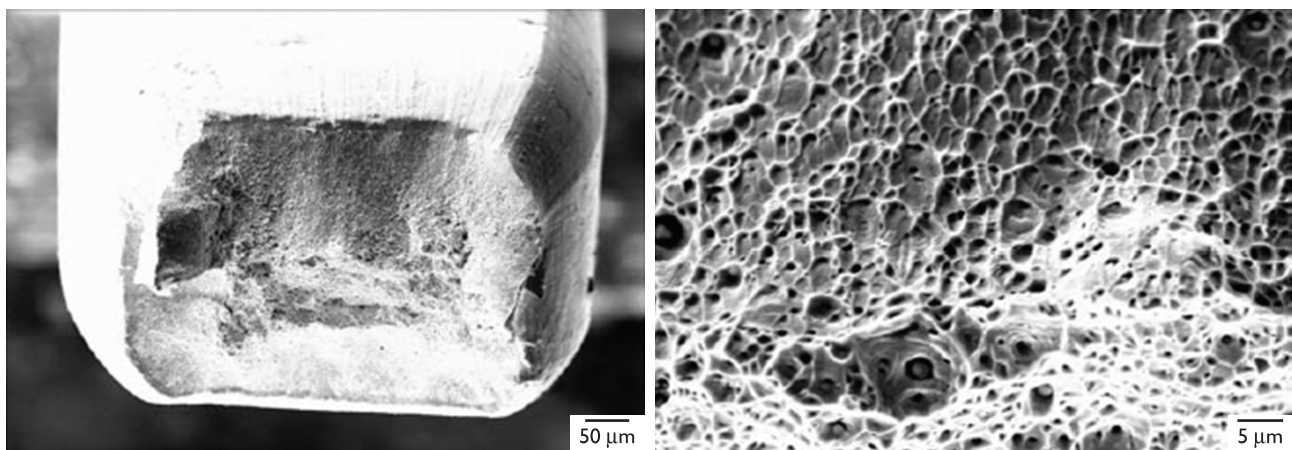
Superfície de fratura obtida pela técnica de microscopia eletrônica de varredura em um fio laminado com seção retangular de 0,483 mm × 0,635 mm.
